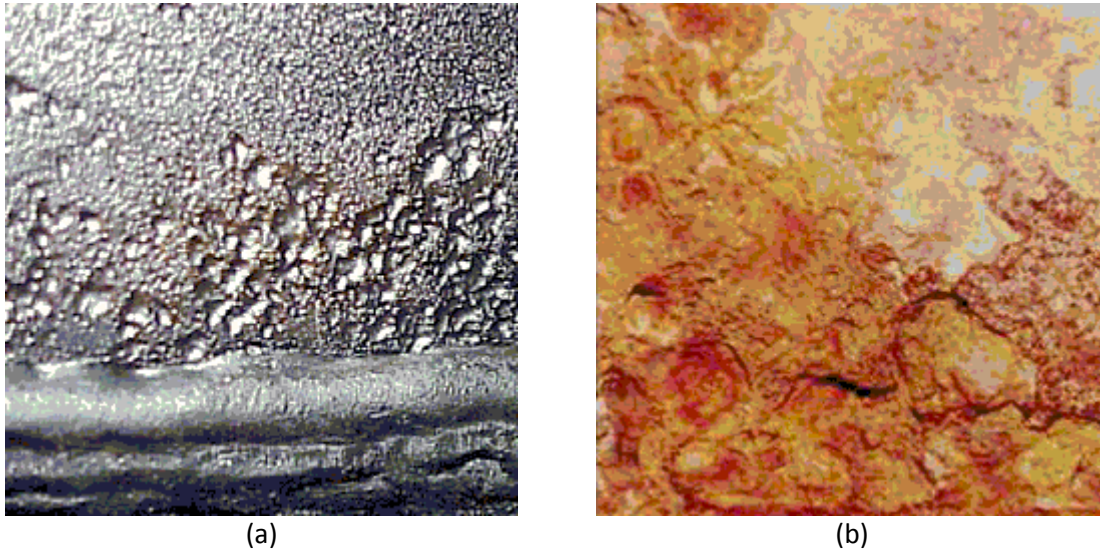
Falhas na tubulação. (a) falha na solda e (b) corrosão generalizada.
